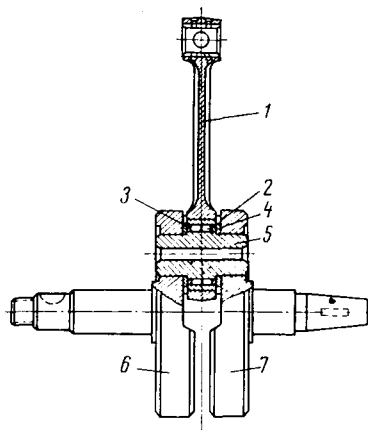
Коленчатый вал двигателя мотороллера Т-200М в сборе:
